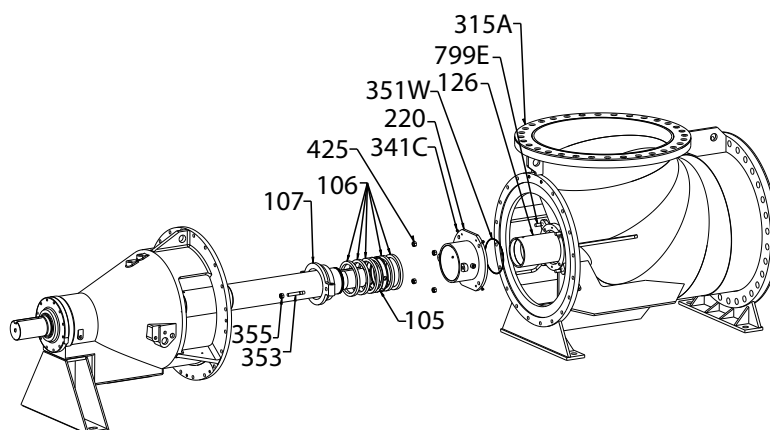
Alineación de la cámara de empaquetadura del eje y casquillo, instalación de la empaquetadura y el anillo de cierre hidráulico
